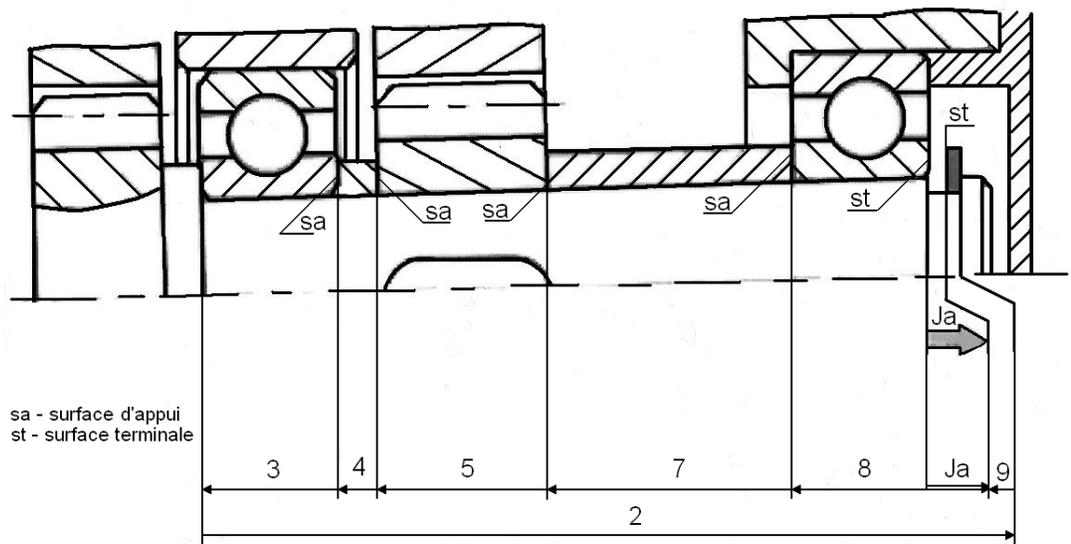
Identification des pièces de l'assemblage mécanique
